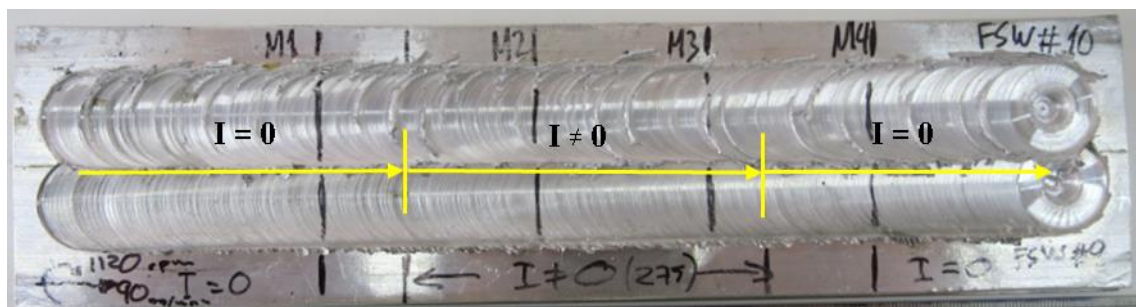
Esquema de troços de soldadura com três zonas
